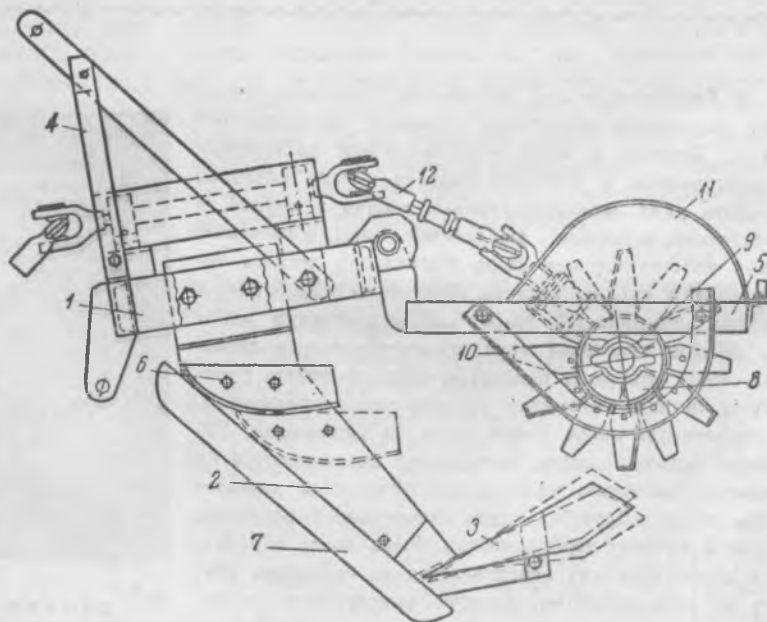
Схема конструкции рыхлителя РЛН-50 (вид сбоку).
